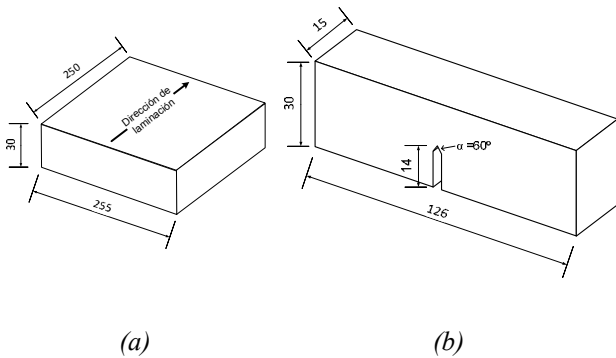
(a) Placas de Al 7017. (b) Geometría final de las probetas de flexión SE. Dimensiones en mm.
